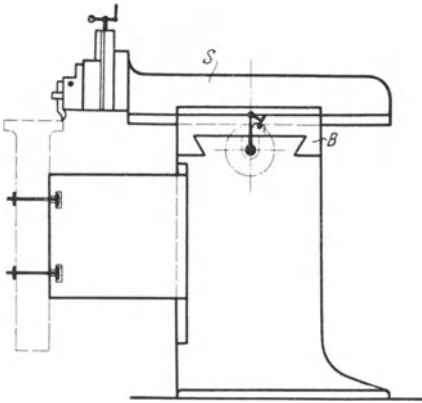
Stößelhobelmaschine mit Querschaltung des Stößels.
